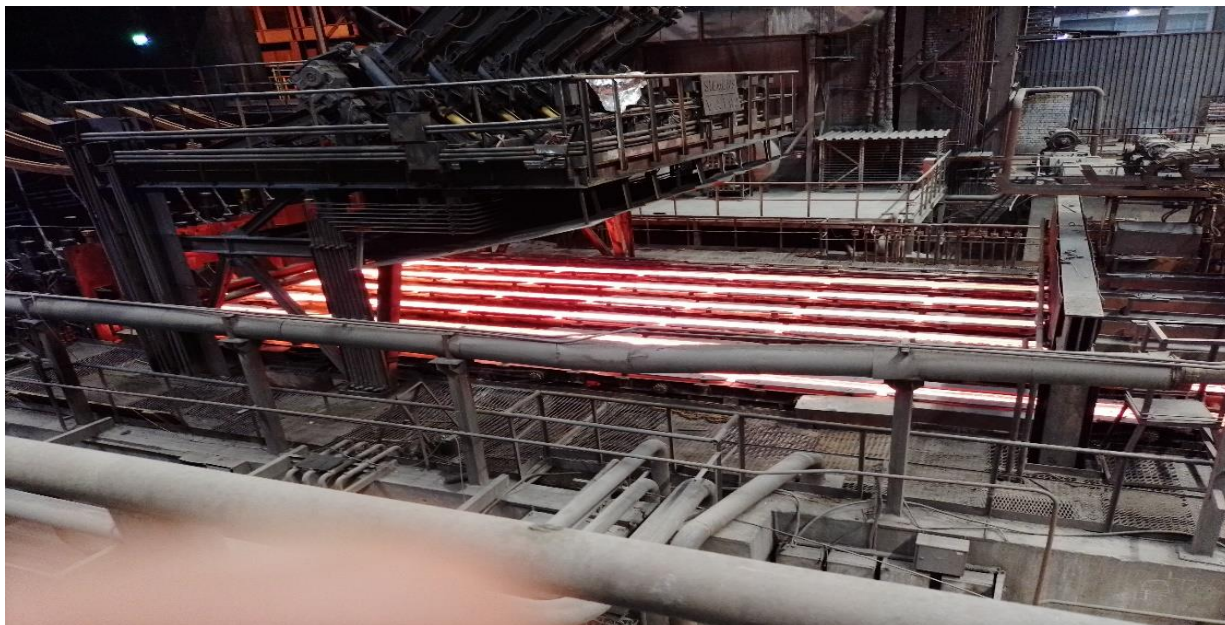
Загальний вид розливки сталеві заготовки на МБЛЗ
